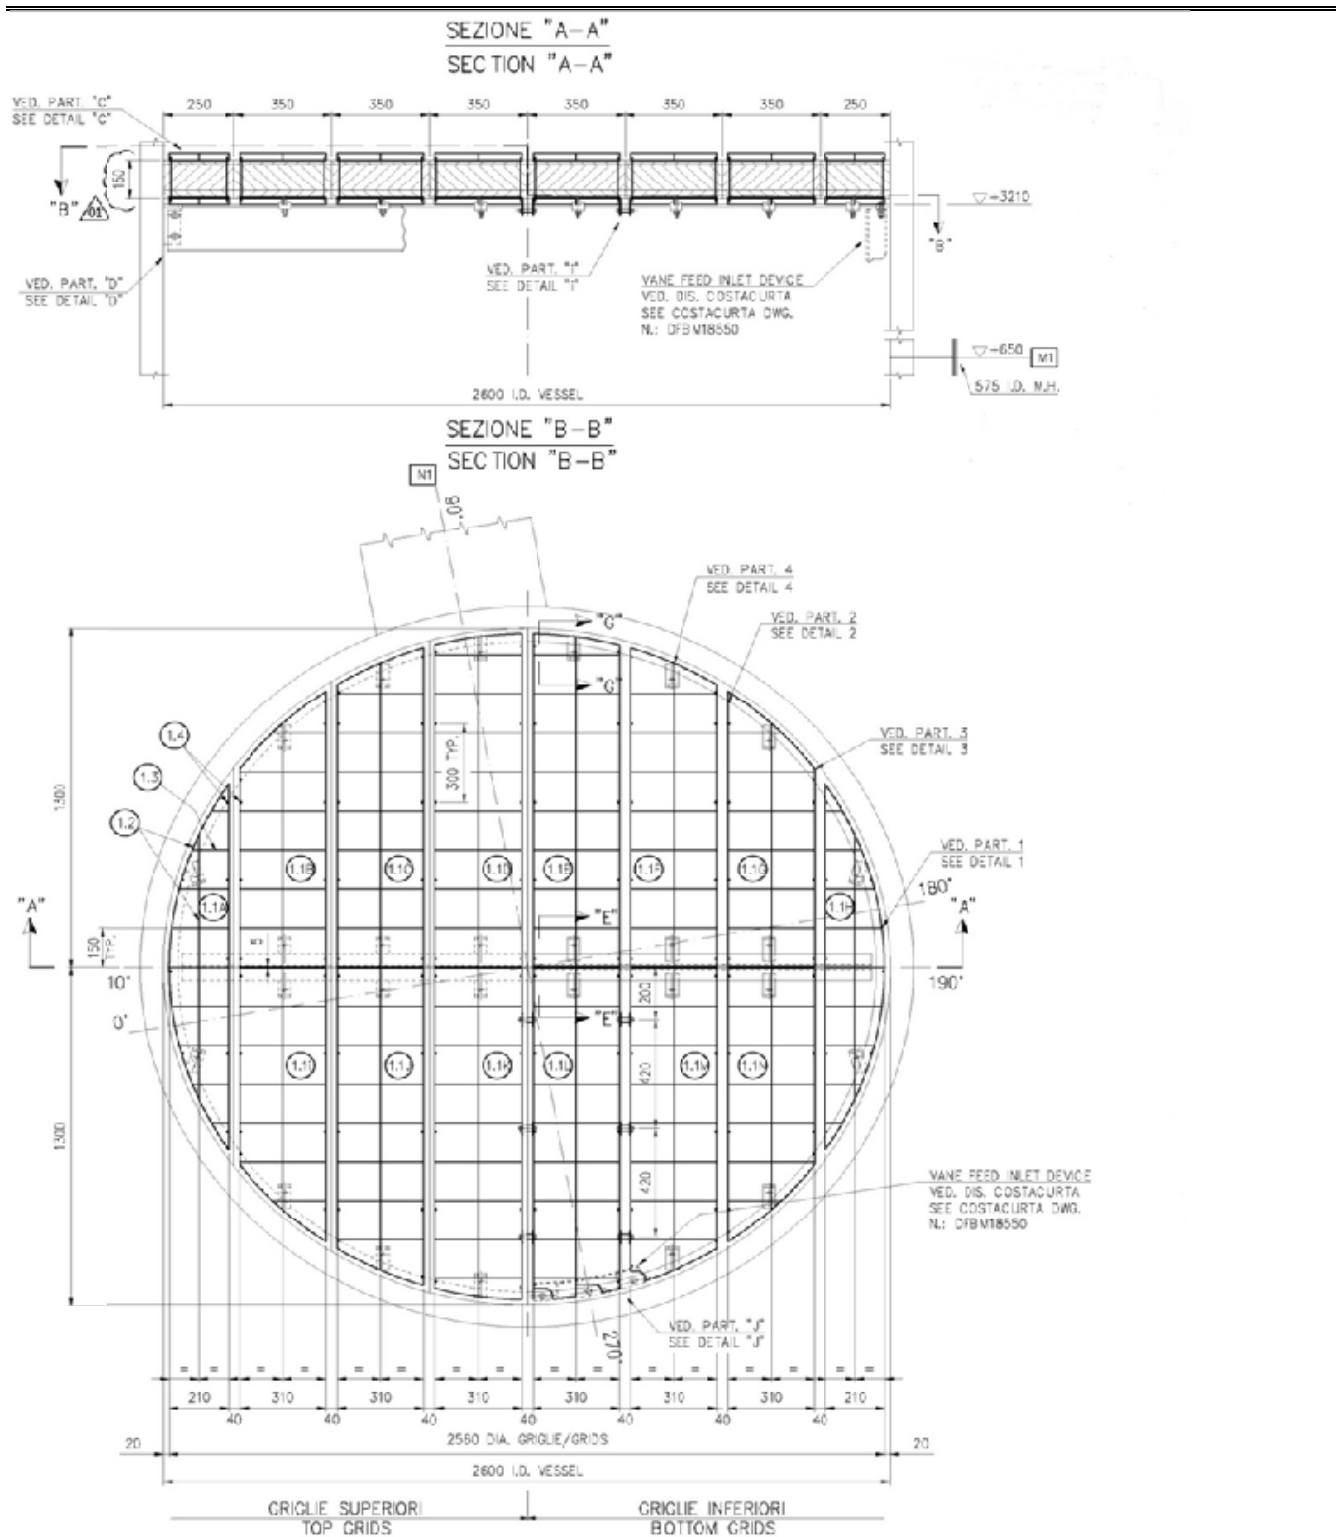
12. .Фрагмент чертежа KE01-A1-P3JM01A-F01-0006-000-PR18042 туманоловителя
